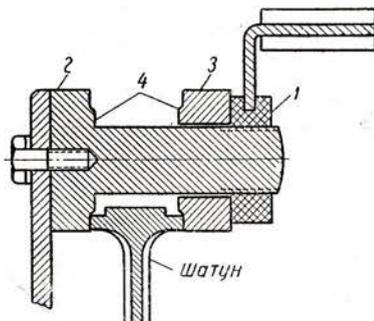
Общий вид прибора для заливки шатунных подшипников J1-3/2
